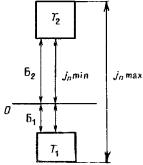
Схема расположения отклонений и допусков, образующих боковой зазор:
